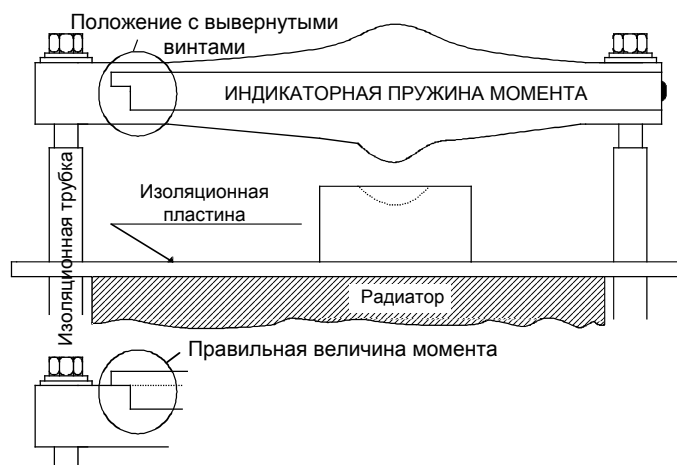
Алюминиевая пружина с приваренной индикаторной пружиной
